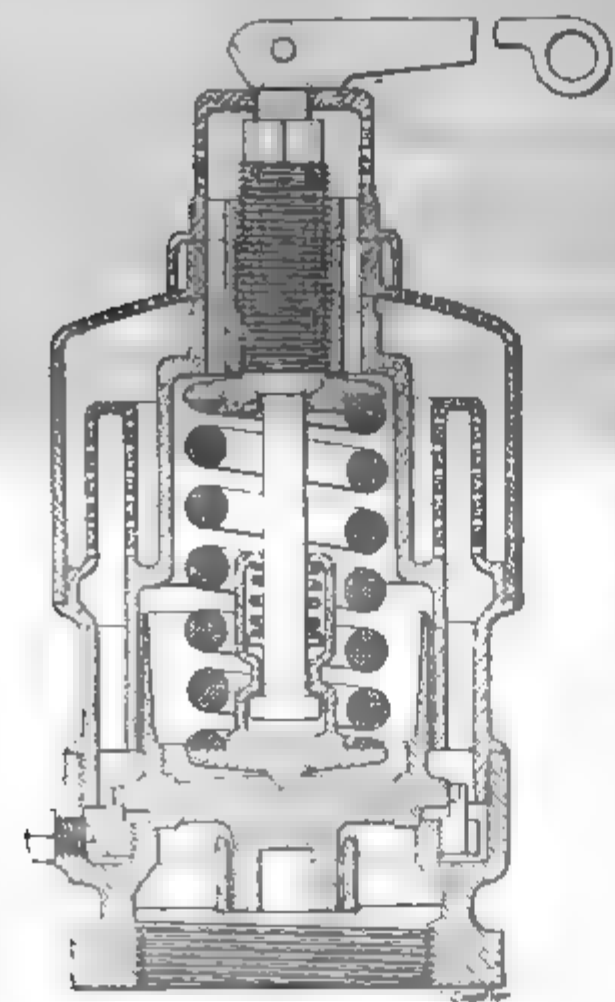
Soupape de sûreté de la Coale Muffler and Safety Valve Co.
